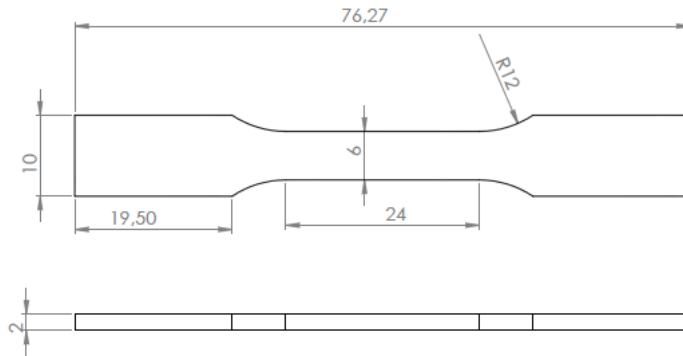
Plan des éprouvettes de traction plane (cotes en mm)
